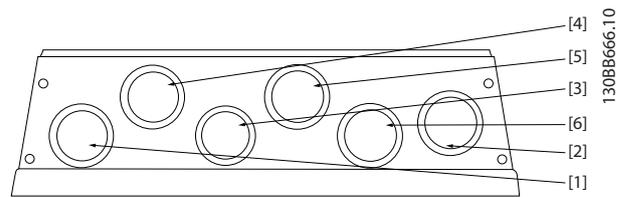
A5 - Kabeleinführungsöffnungen mit Gewinde IP55
